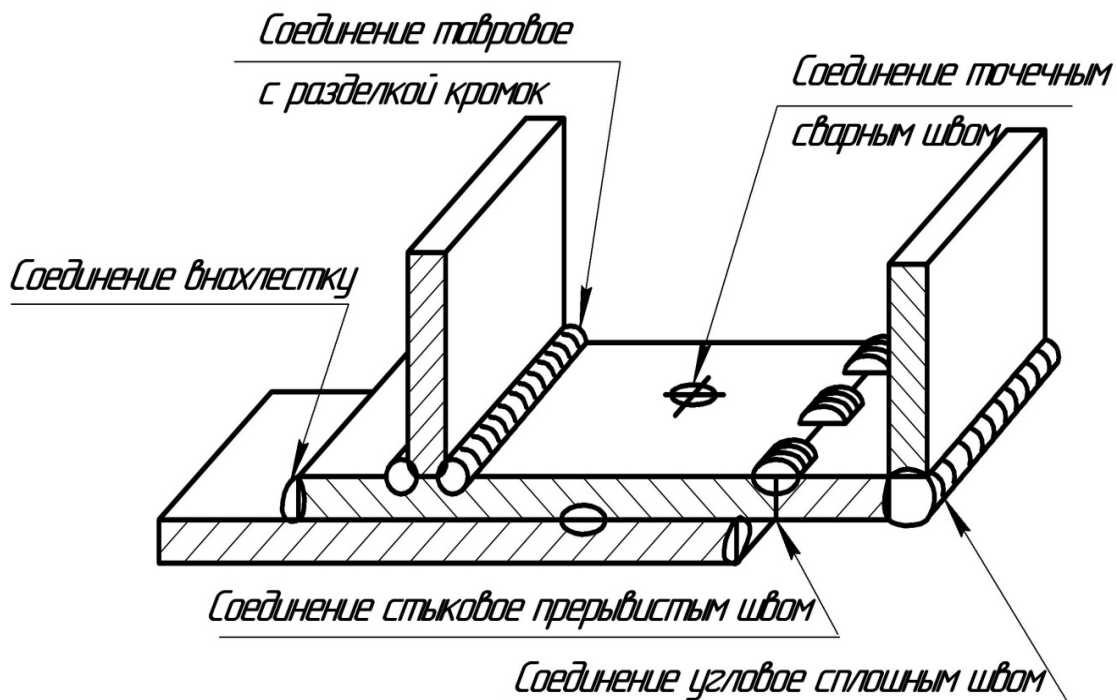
Типы сварных соединений и швов
